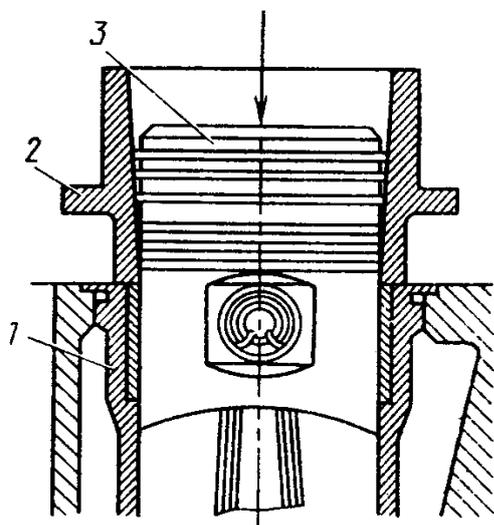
Установка поршня в сборе с кольцами и шатуном в цилиндр: 1-гильза блока цилиндров; 2-приспособление (оправка); 3-поршень в сборе с кольцами и шатуном
